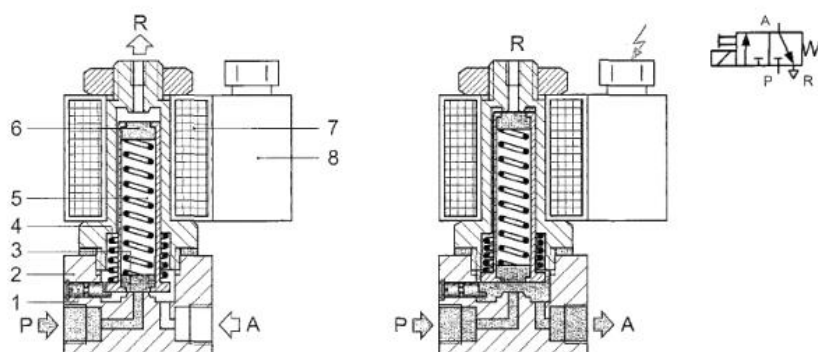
3/2-пневмораспределитель с электромагнитным управлением и ручным дублированием (конструкция и условное графическое обозначение на схемах): 1 – поворотное устройство; 2 – корпус; 3, 6 – седло клапана; 4 – пружина; 5 – якорь; 7 – катушка; 8 – коннектор
